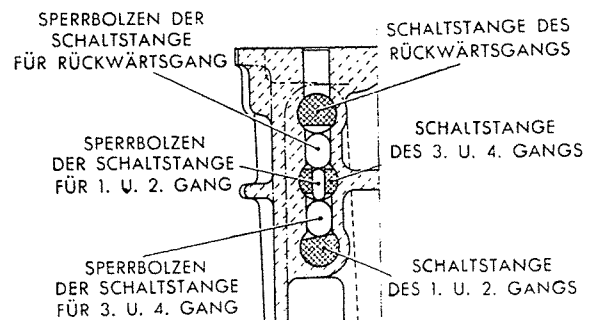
Teilschnitt des Wechselgetriebes durch die Sperrbolzen der Schaltstangen.
